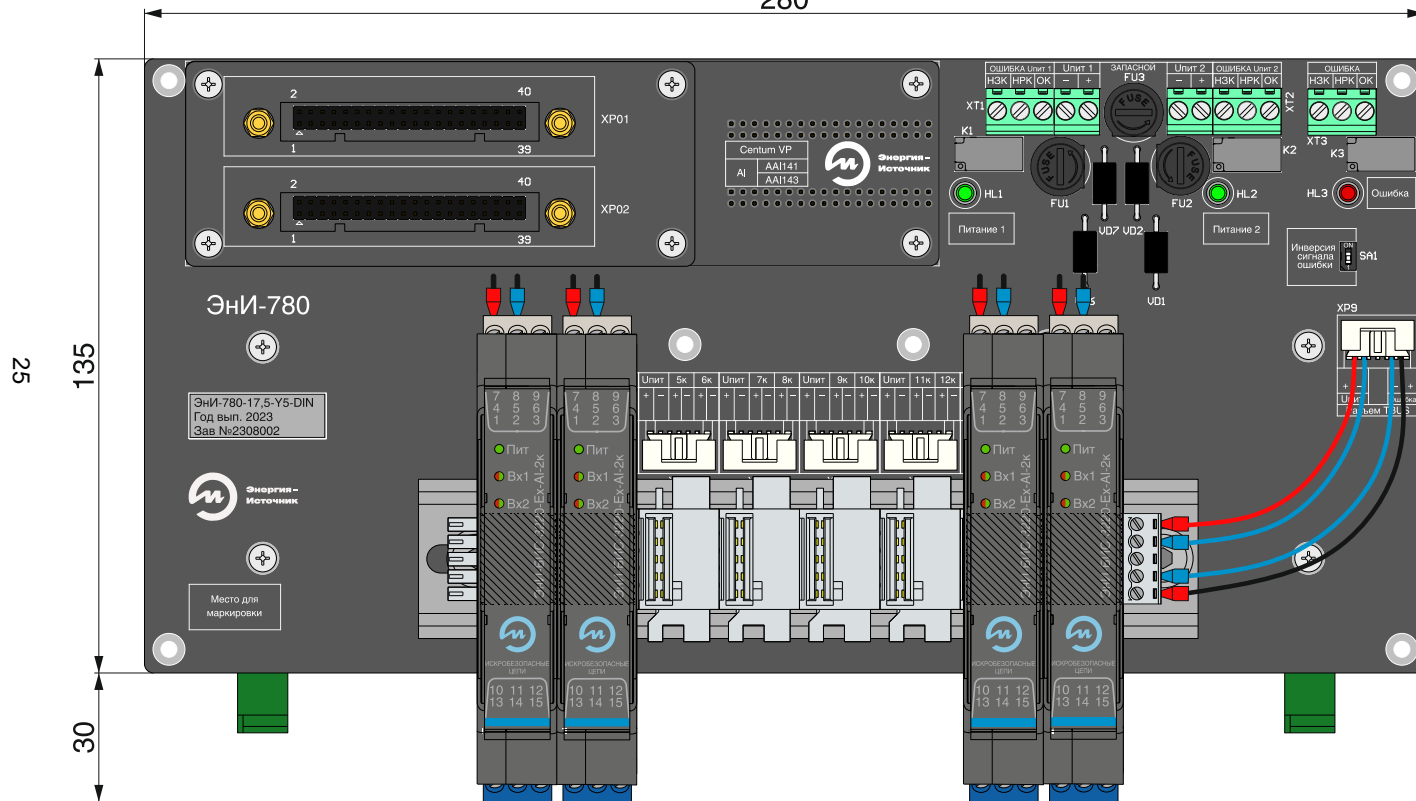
Габаритные размеры платы для восьми приборов с корпусом шириной 17,5 мм
